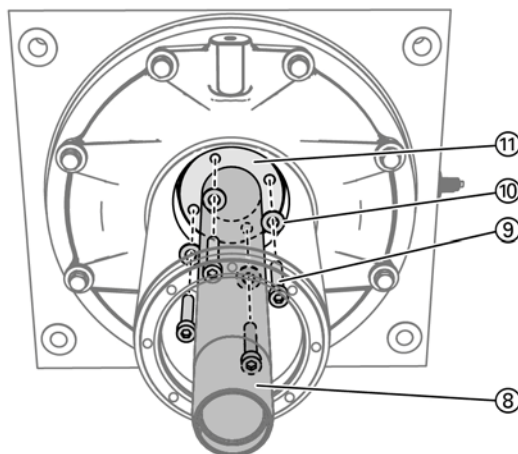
Откручивание крышки корпуса отсека подключения ячейки
